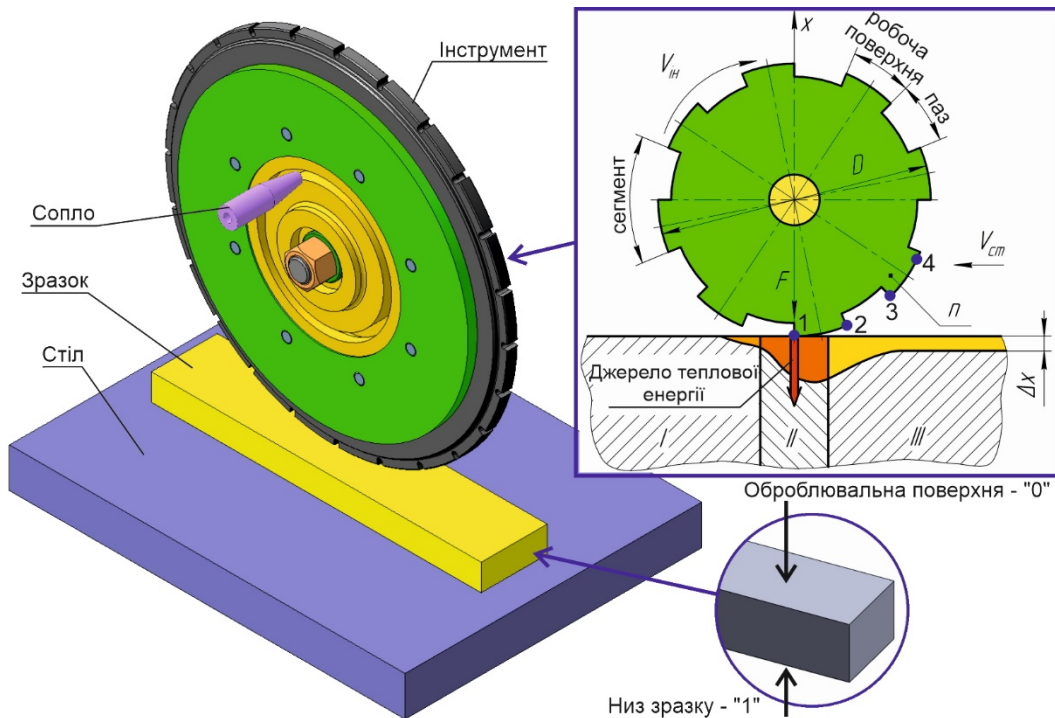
Область оброблення під час фрикційної обробки плоских поверхонь: 1 – ділянка перед зоною оброблення; 2 – ділянка безпосереднього контакту; 3– ділянка за зоною контакту інструмент-деталь
